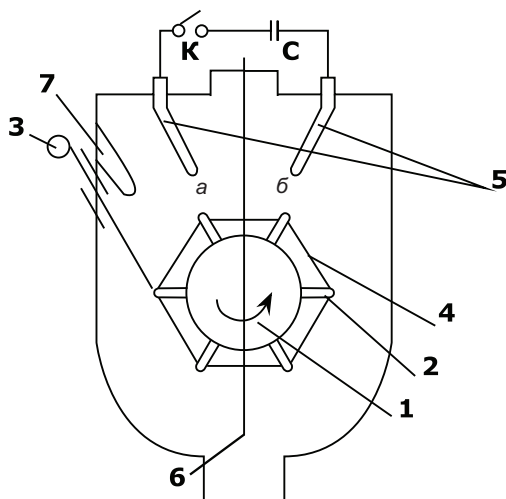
Устройство автоматической подачи цилиндрической иницирующей вставки:
